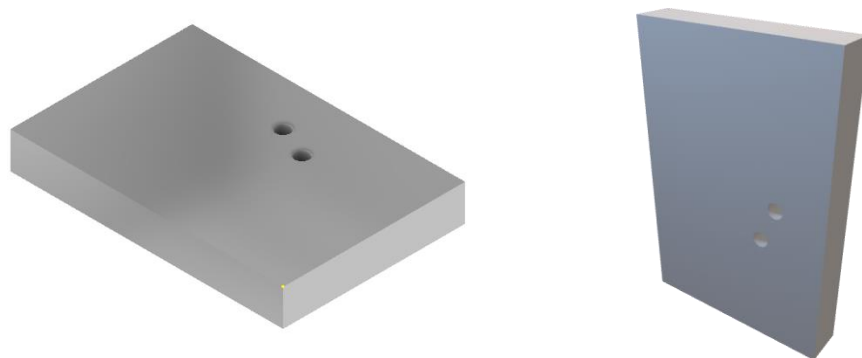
Τρισδιάστατη απεικόνιση αποστολής 25
